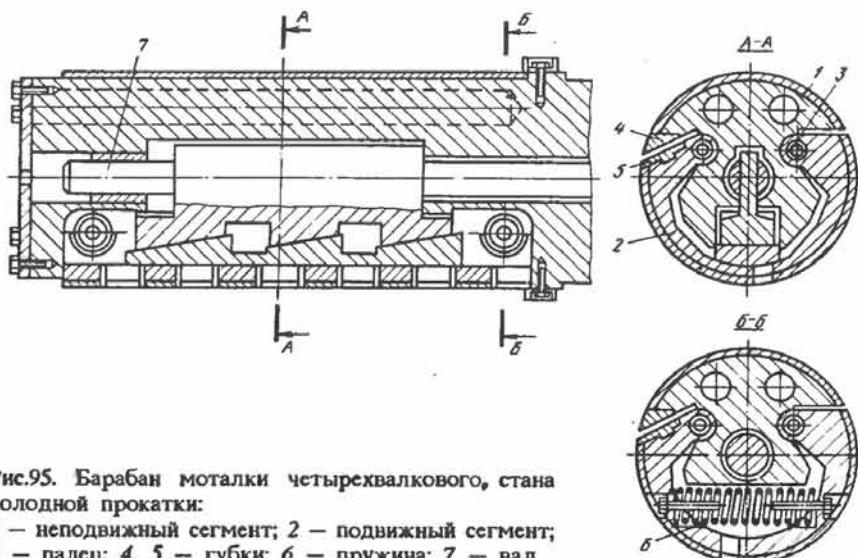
Барабан моталки четырехвалкового, стана холодной прокатки:
